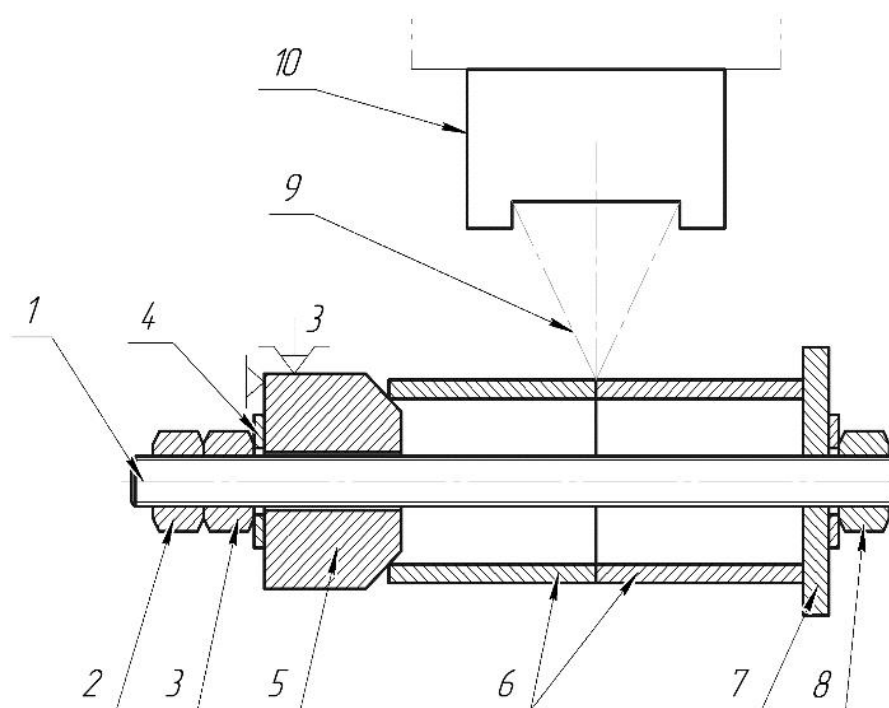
Приспособление для лазерной сварки труб. 1 – Шпилька, 2 – Гайка, 3 – Контр-гайка, 4 – Шайба, 5 – Конусный упор, 6 – Стыкуемые трубы, 7 – Зажимная шайба, 8 – Зажимная гайка, 9 – Схема фокусировки лазера, 10 – Лазерная сварочная голова Kugler.
